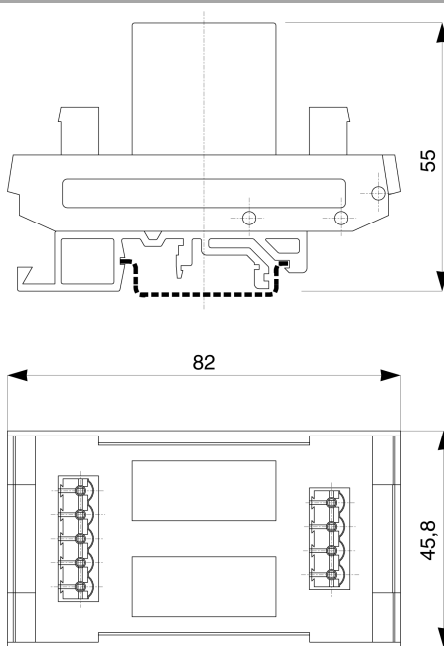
dimensioni meccaniche del modulo a relè SB300
